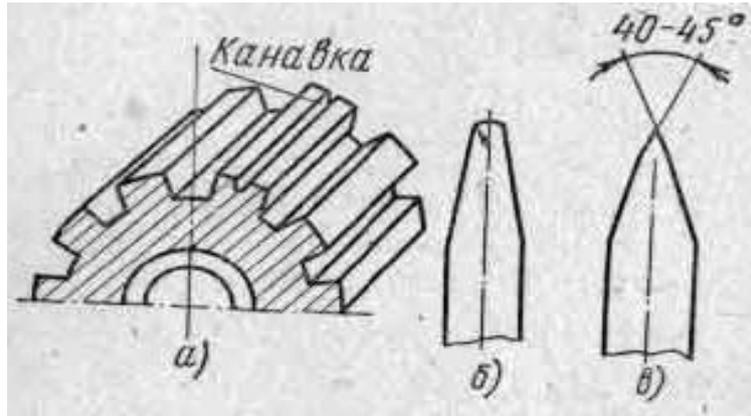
Ремонт шлицев раздачей: а) Канавка, после проходки резцом или зубилом; б) чекан; в) зубило с углом режущей кромки не более 40-45°
